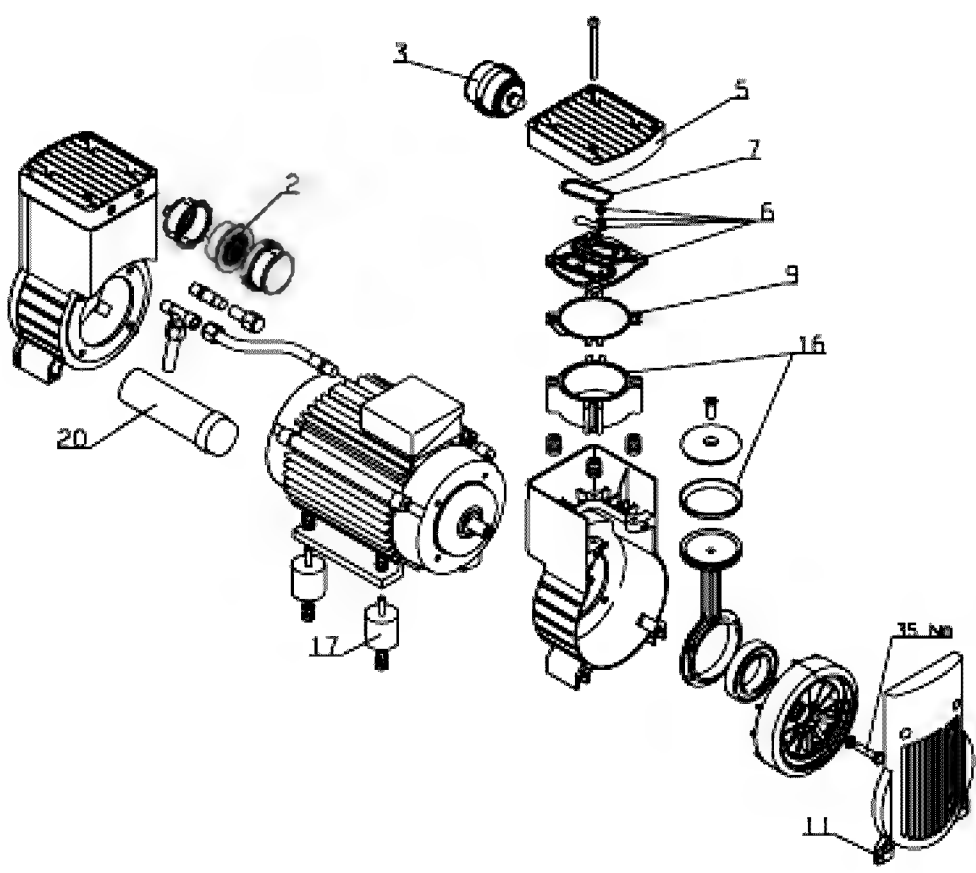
Чертеж составных частей компрессора D-100
